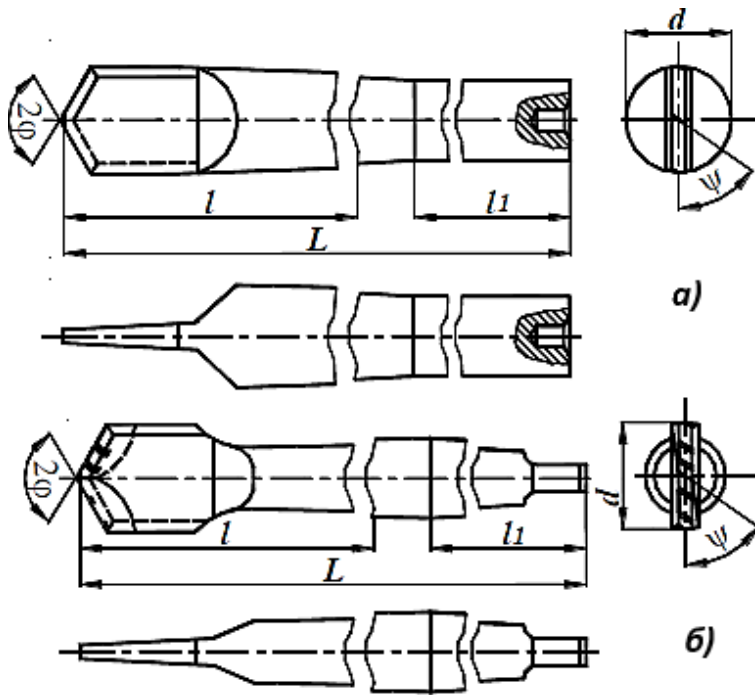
Конструкція цілісного (зварного або напаяного) перового свердла з швидкорізальної сталі:
